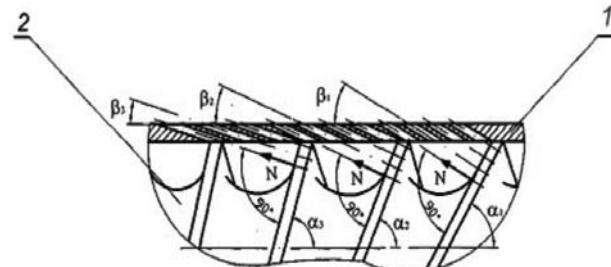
Схема расположения отверстий в перфорированной втулке шнекового обвалочного пресса:
